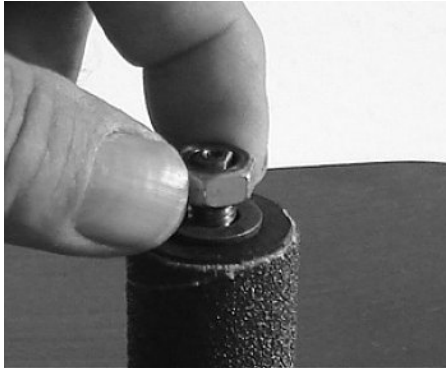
Spindelscheibe aufsetzen und Mutter aufschrauben
